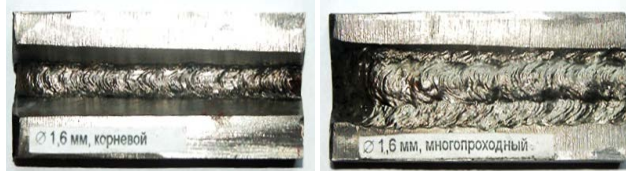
Зовнішній вигляд зварних швів при мокрому підводному зварюванні високолегованої корозійностійкої сталі типу 18-10
